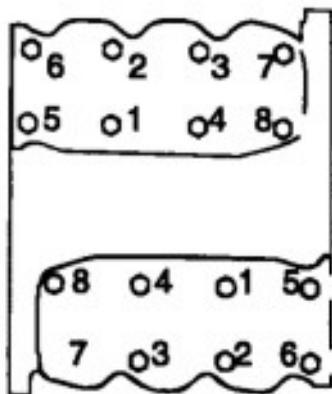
Порядок затягивания болтов крепления головки блока цилиндров
